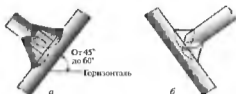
Сварка таврового соединения «в лодочку»
